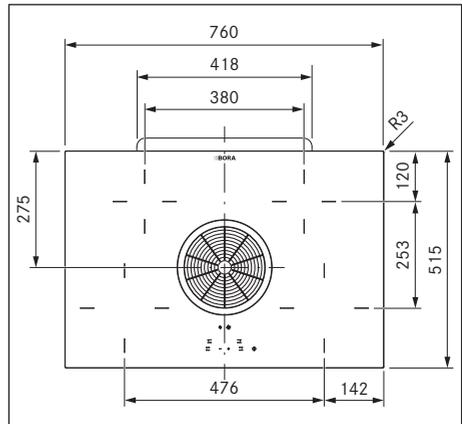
BHA dimensioni apparecchio vista dall'alto
